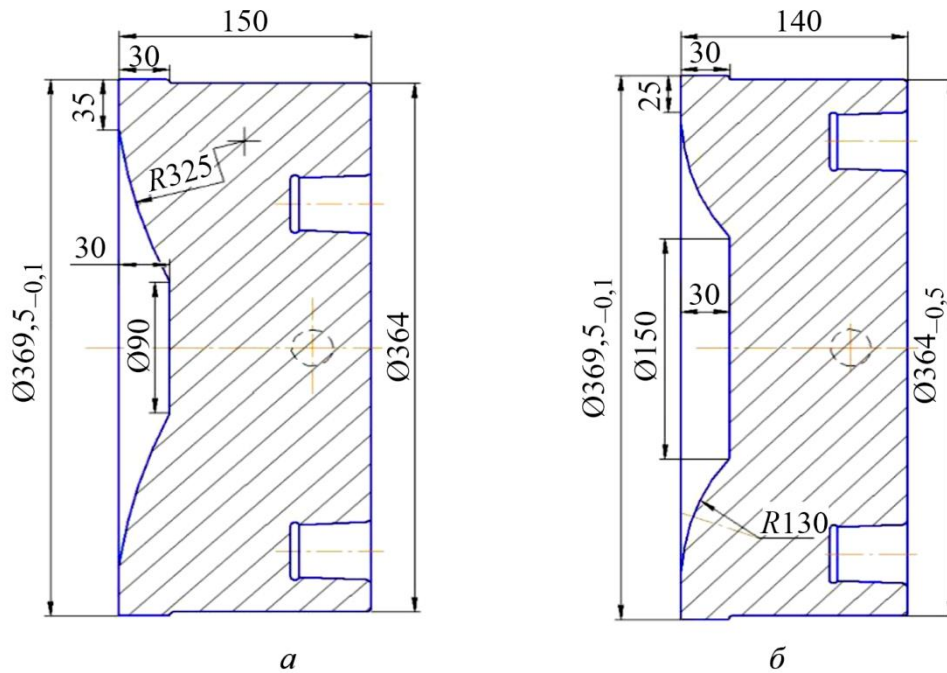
Конструкция пресс-шайб: пресс-шайба № 1 (а); пресс-шайба № 2 (б)
